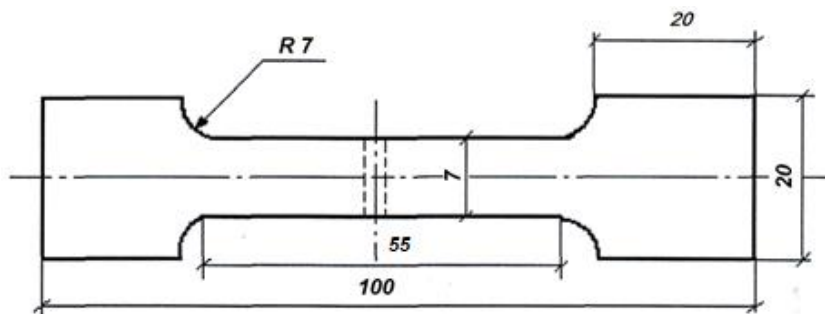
Размеры и форма образца; толщина 3 мм, штриховыми линиями отмечена зона сварного шва
